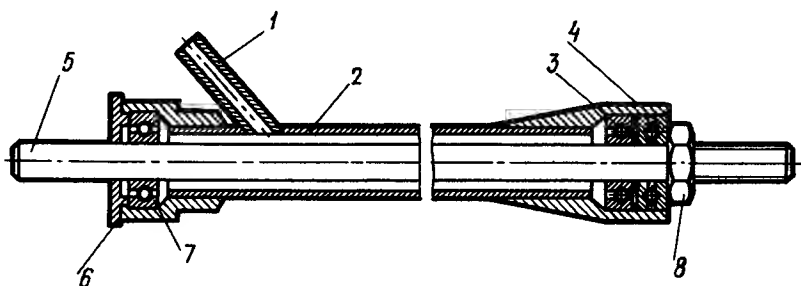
Дейдвудная труба с тремя шариковыми подшипниками:
